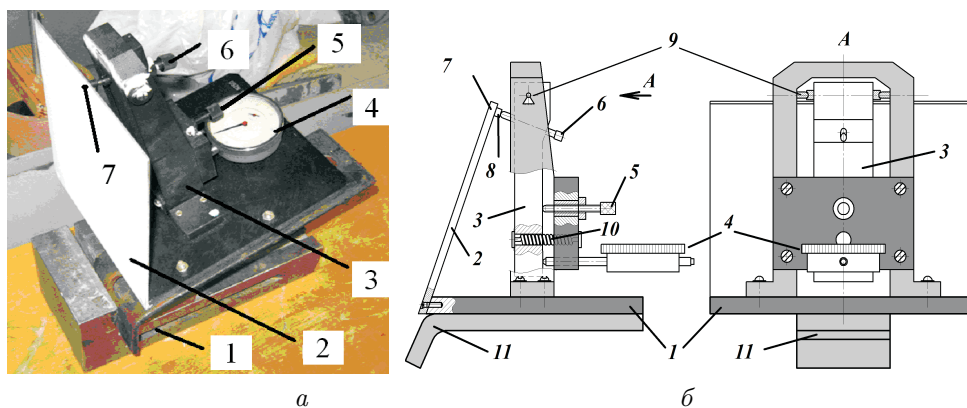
Общий вид поверочного устройства ОМ-3 (*а*) и схема его конструкции (*б*): *1* — основание; *2* — рабочая пластина; *3* — рычажная система; *4* — стрелочный индикатор; *5* — нагрузочный винт; *6* — опорный винт; *7* — контрольная точка; *8* — контактный элемент; *9* — поворотная ось; *10* — возвратная пружина; *11* — дополнительная пластина
